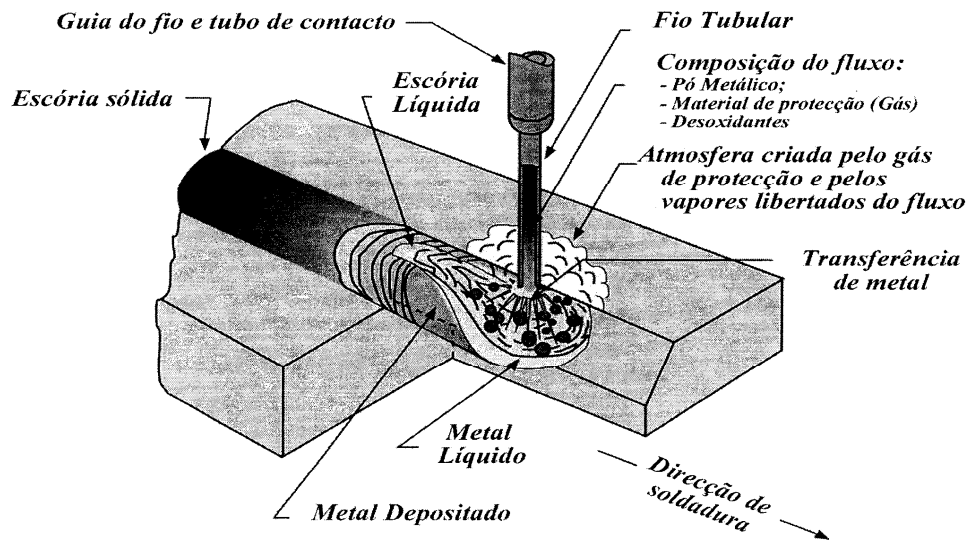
Esquema de soldadura do processo FCAW
